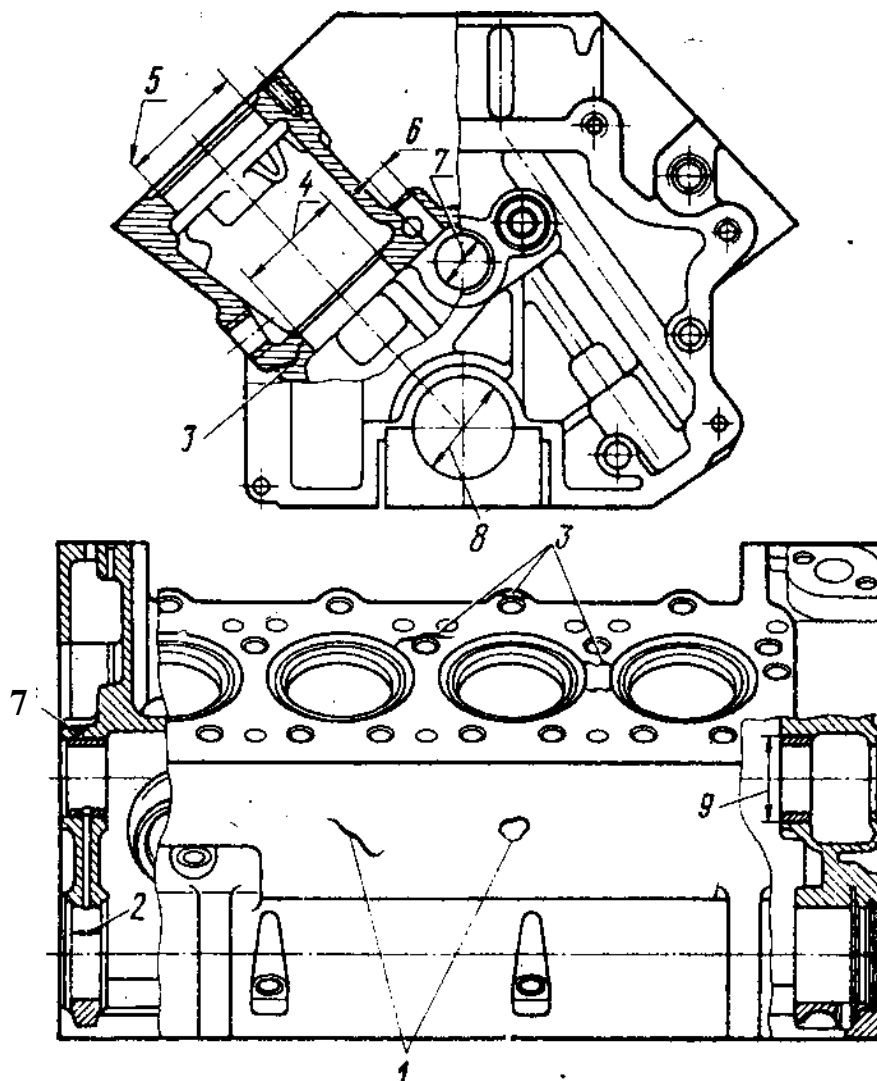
Основные дефекты блока цилиндров на примере двигателя ЗИЛ-130
